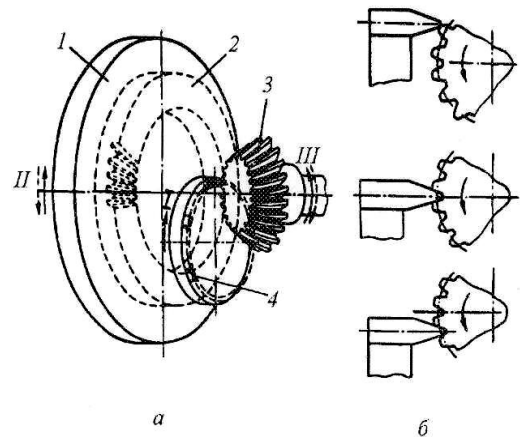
Схема нарізування конічного колеса з круговими зубами торцевою зуборізною голівкою
